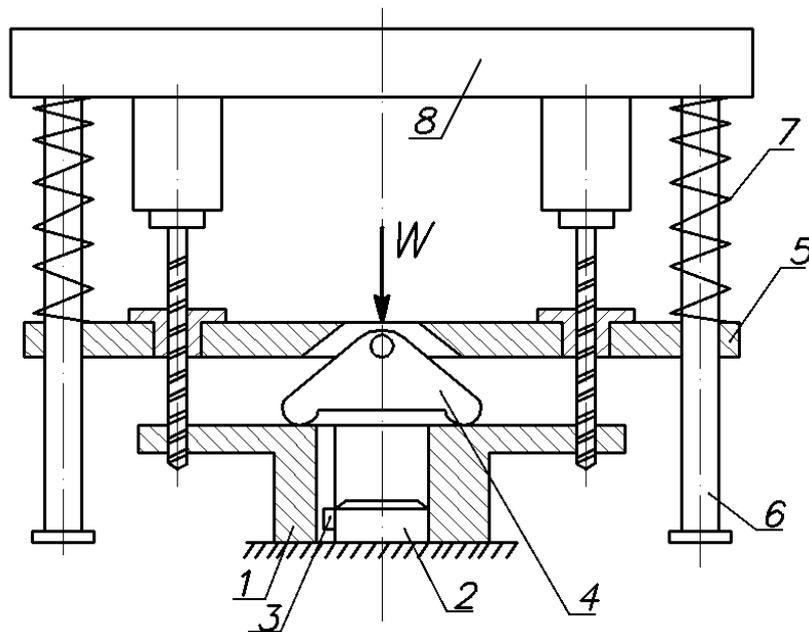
Схема сверлильного приспособления с пружинным зажимом.
